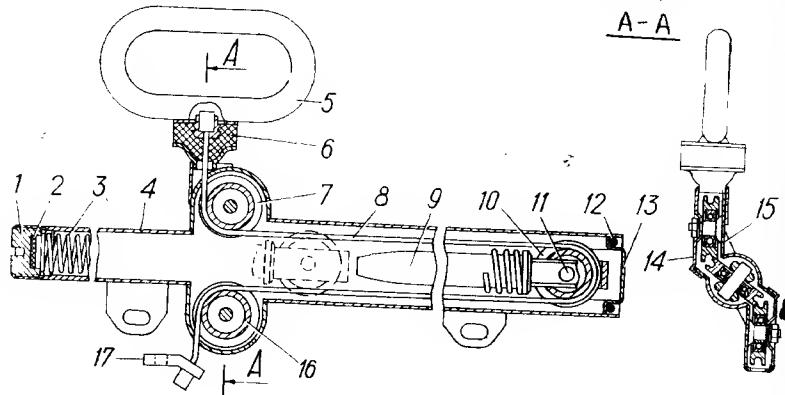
Механизм привода нижней створки боковой двери (тросоукладчик):
